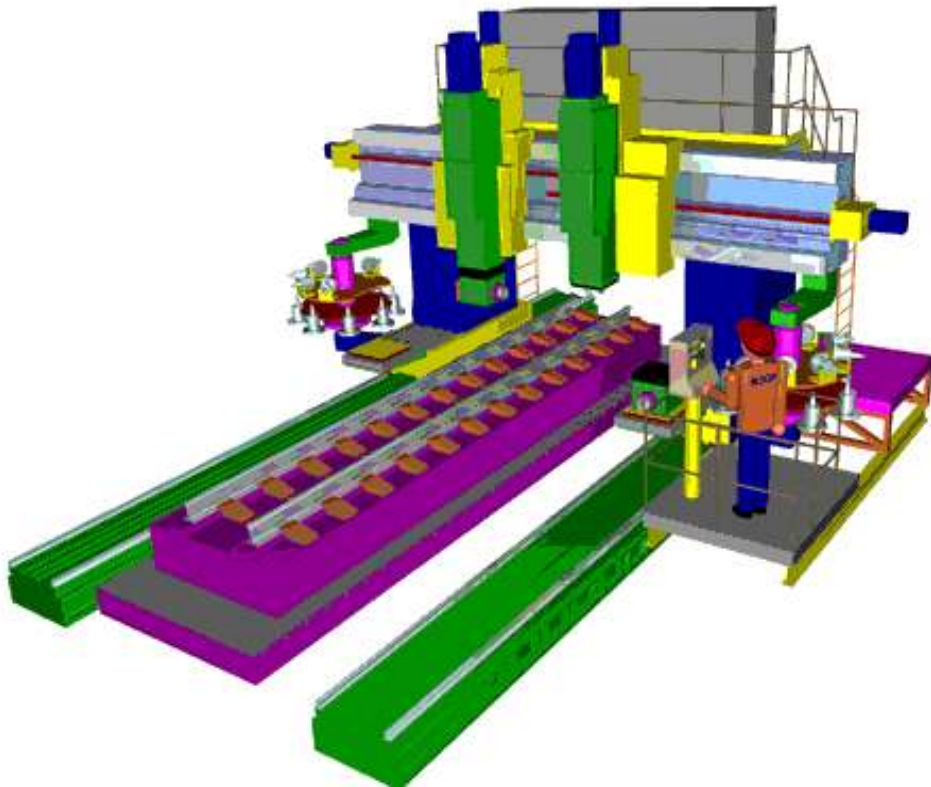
Продольный фрезерно-расточной станок с ЧПУ
